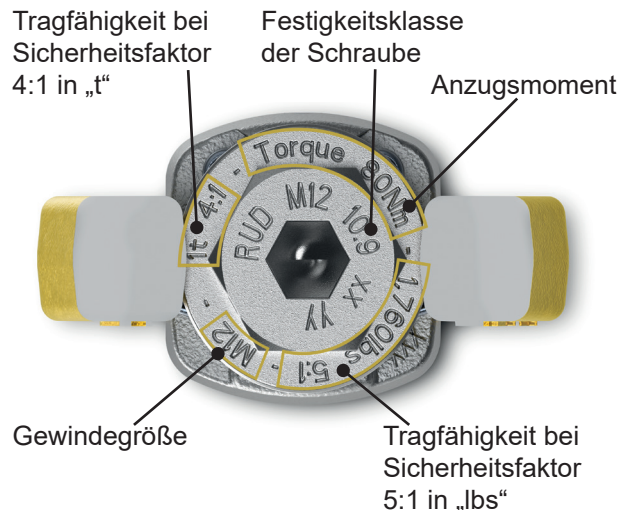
ACP-TURANDO OCEANSTAR M8-M30 - Kennzeichnung Buchse / Schraube
